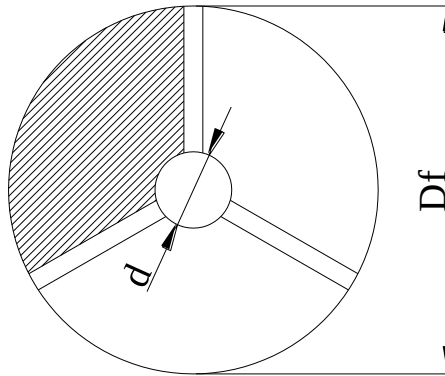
Corte transversal de la despulpadora. Fuente. Propia.
